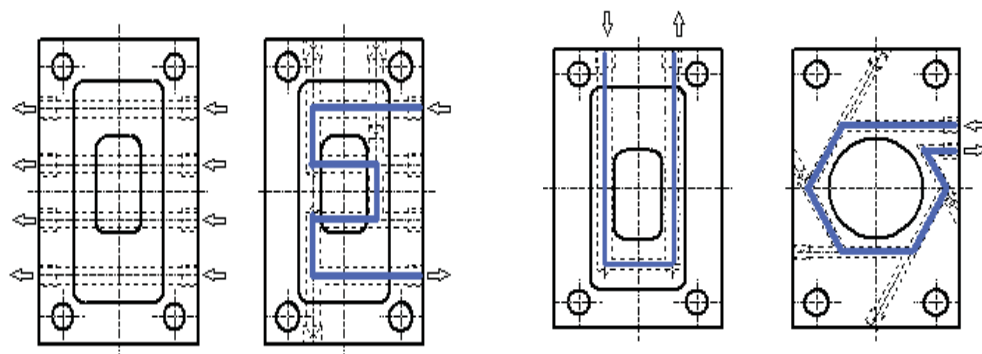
Circuit de refroidissement des plaques de moules. [28]
